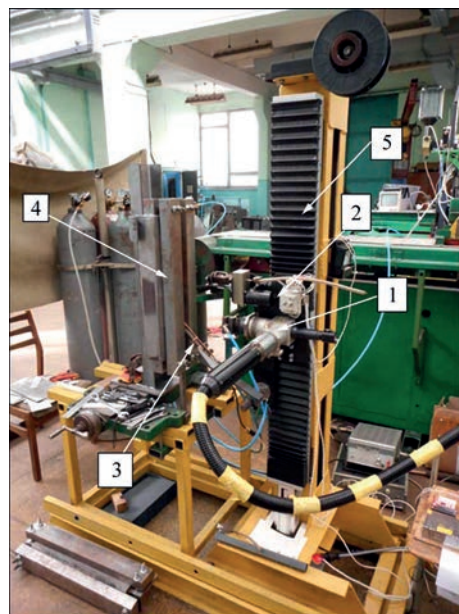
Частина лабораторного стенду для відпрацювання технологічних прийомів лазерного зварювання у вертикальному просторовому положенні: 1 – головка для лазерного зварювання; 2 – каретка маніпулятора; 3 – газовий захист; 4 – трубуцина; 5 – балка маніпулятора (вісь Z)
